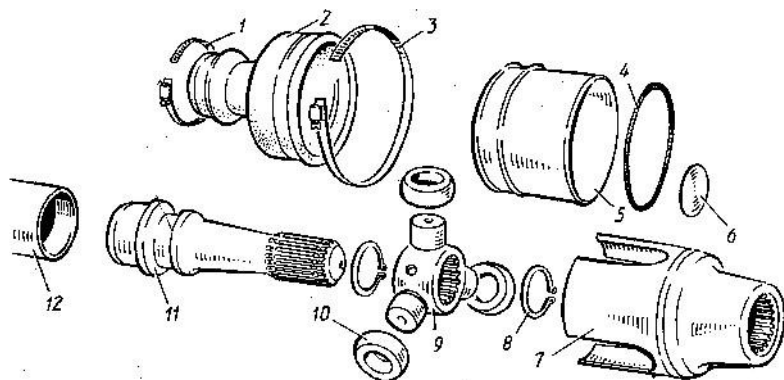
Детали подвижного шарнира трипод фирмы «Гленсер-спайсер». Труба 12 служит полуосью и сварена с цапфой 11. Цапфа 11 мелкошлицевым профилем соединяется со звездочкой 9 трипода; три ролика 10 входят в выемки корпуса 7 шарнира и передают крутящий момент в этой «открытой» конструкции. Внешнюю грязезащиту осуществляют уплотнительное кольцо 4, крышка 5 и чехол 2; изнутри отверстие закрывается крышкой 6. Хомуты 1 и 3 крепят чехол, а стопорные кольца 8 — звездочку. Этот шарнир допускает углы до 22° , перемещение до 55 мм и крутящие моменты до 4,2 кН·м. Чтобы обеспечить требуемую плавность вращения, угол в шарнире не должен превышать в продолжительном режиме 4° .
